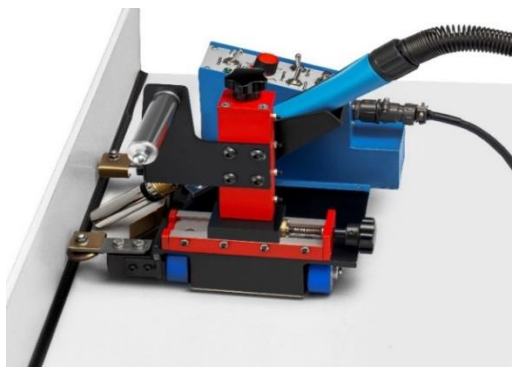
Тележка КС-5 для перемещения сварочных горелок
